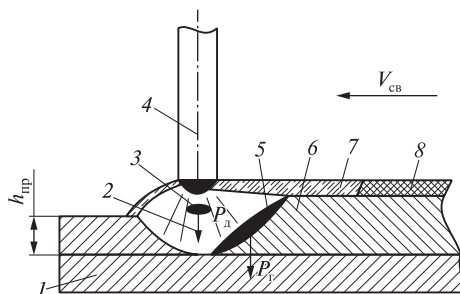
Схема строения сварочной ванны и формирования сварного шва:
